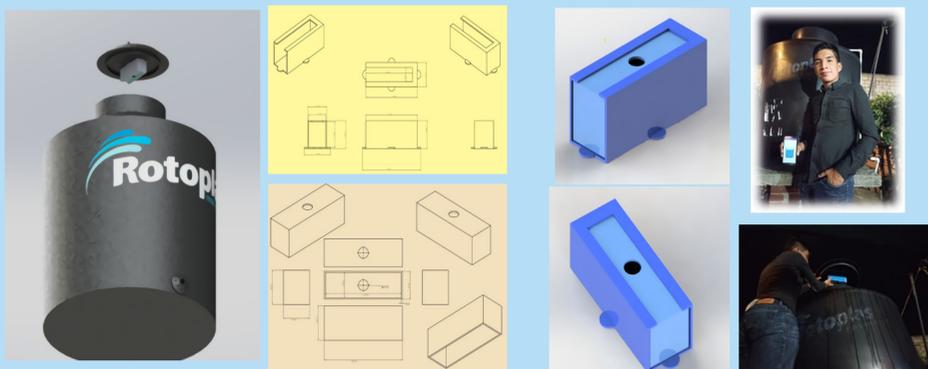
Diseño mecánico de prototipo en SOLIDWORKS.
